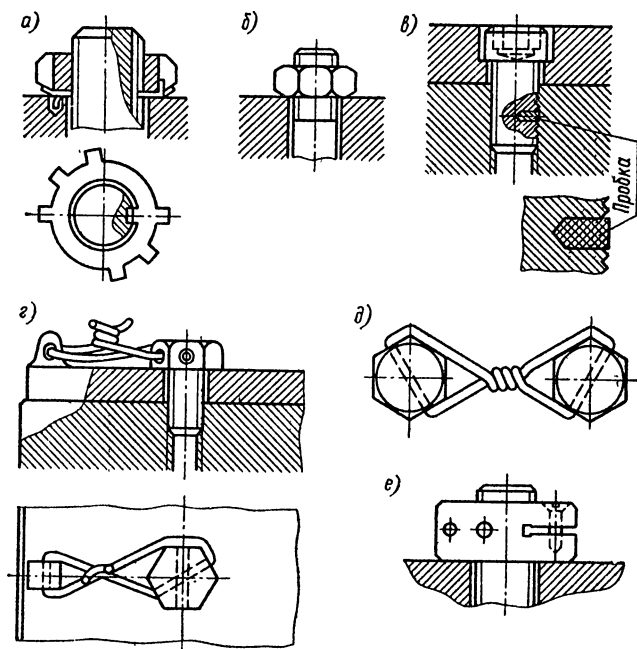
Примеры стопорения резьбовых соединений: а — шайбой; б — сваркой (накерниванием); в — пробкой из упругого материала; е — с использованием специальных гаек; г, д — проволокой
